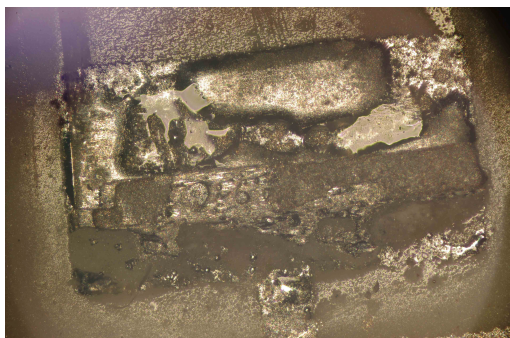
Detailní pohled na zapájený rezistor typu 0402, pájeno na vzduchu, pasta SAC305.
